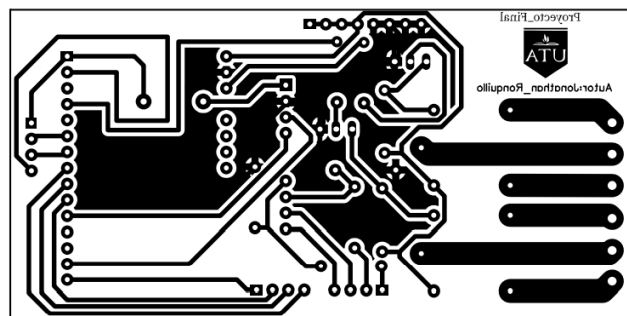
Circuito impreso junto a la máscara de soldadura.
